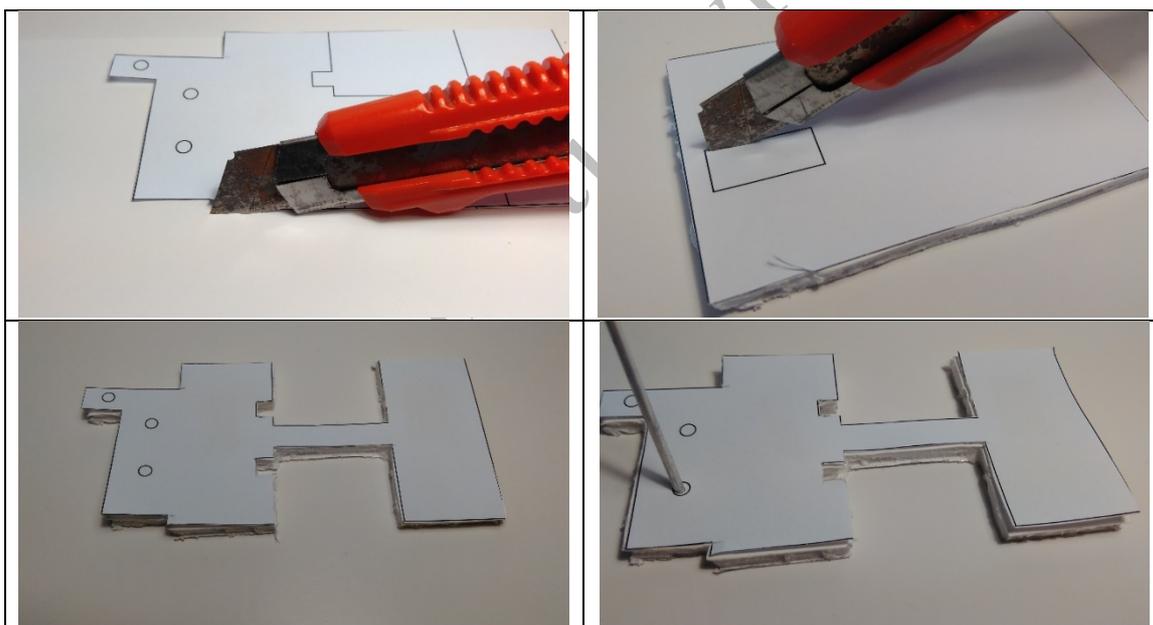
Creación de las piezas utilizando las plantillas
